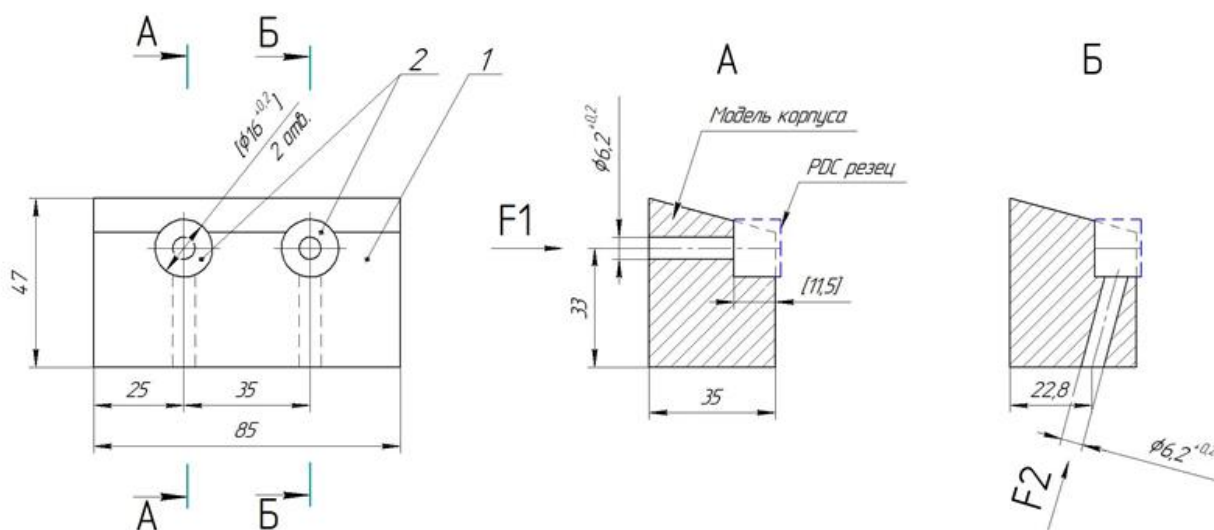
Эскиз модели корпуса опытного долота для испытаний пайки PDC резца
